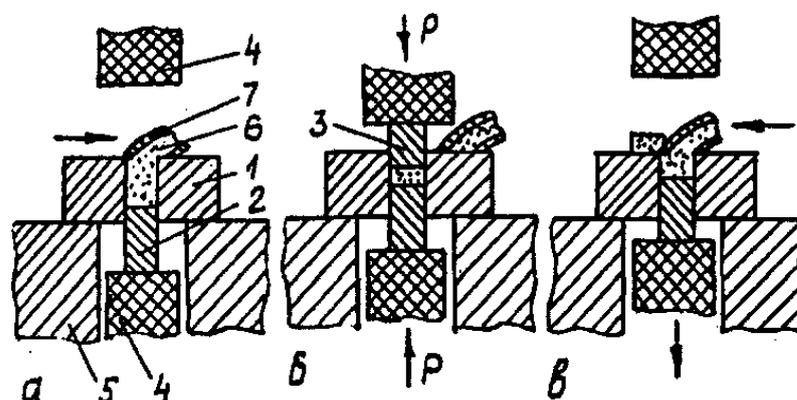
Схема прессования металлического порошка с объемной автоматической дозировкой: а - засыпка порошка в матрицу; б - прессование; в - выпрессовывание порошковой формовки; 1 - матрица; 2,3 - пуансоны; 4 - плунжер пресса; 5 - плита пресса; 6 - порошок; 7 - питатель
